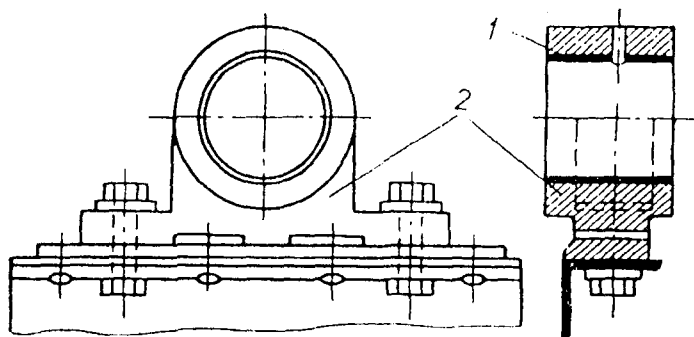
Подшипник скольжения глухой: 1 – антифрикционная втулка; 2 – корпус подшипника.
